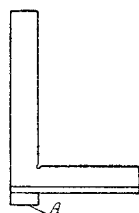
Схема проверки совмещения привалочных плоскостей штамподержателя и бабы приспособлением.
